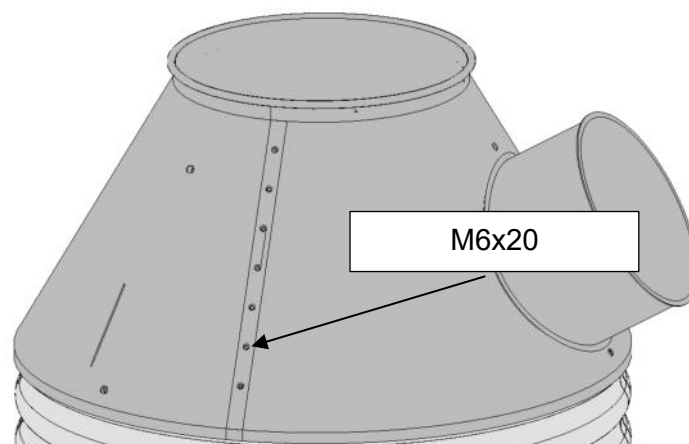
Болтовое соединение верхнего конуса друг с другом.
